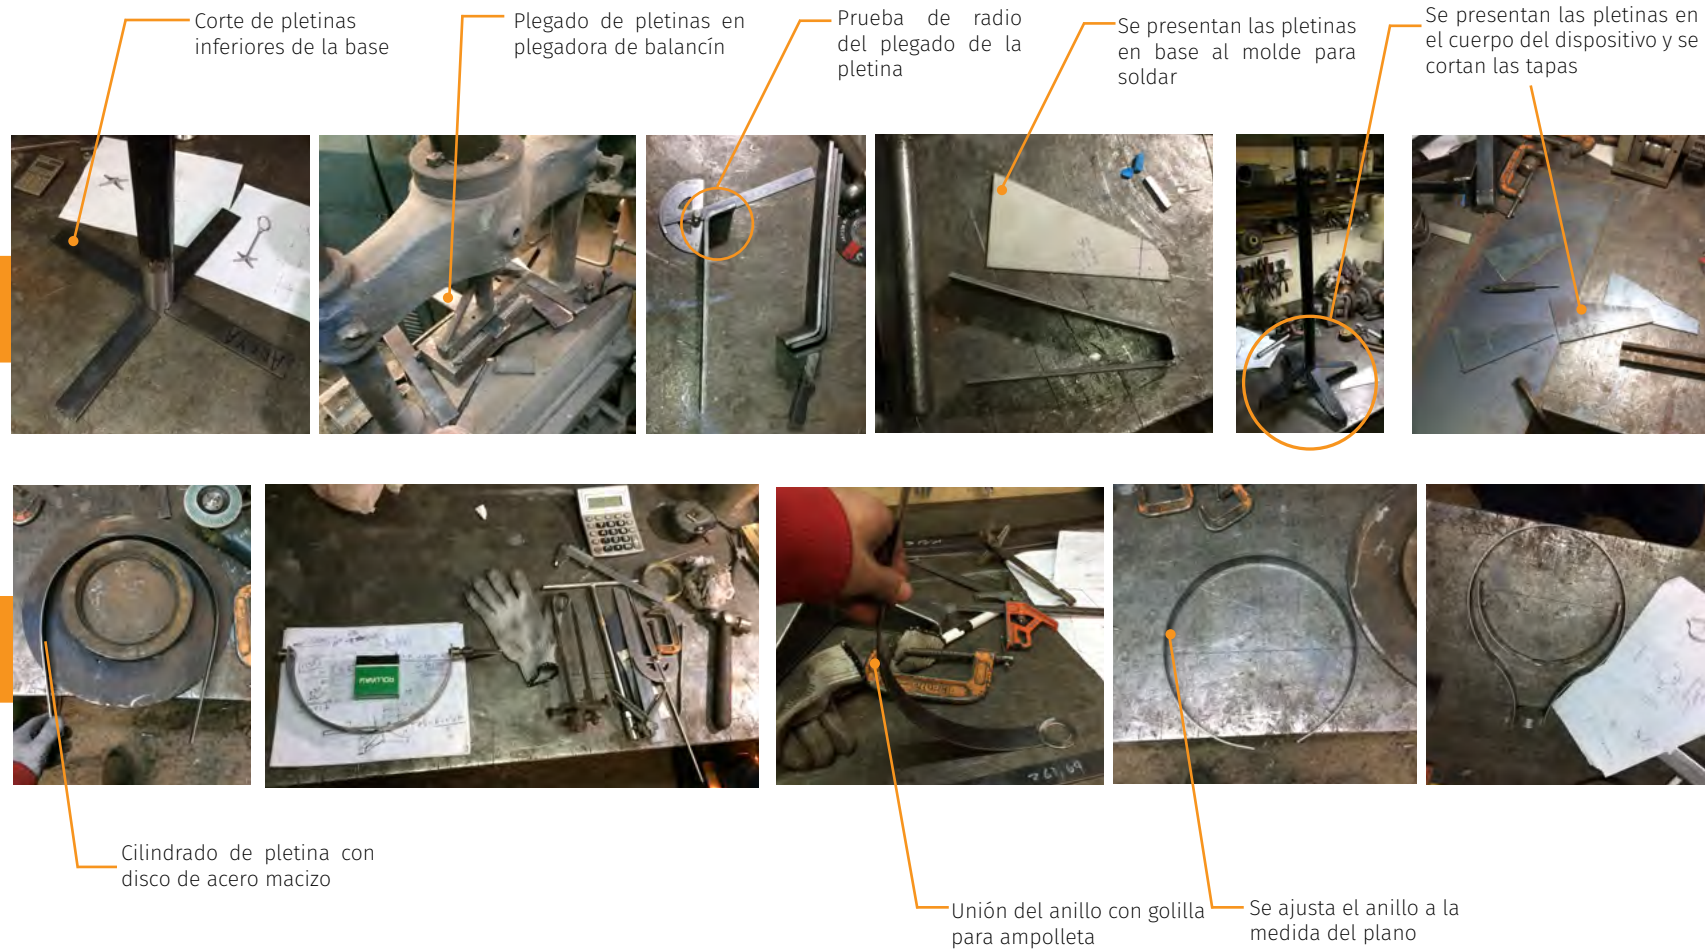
Fabricación. Desarrollada por el autor. [Esquema].
